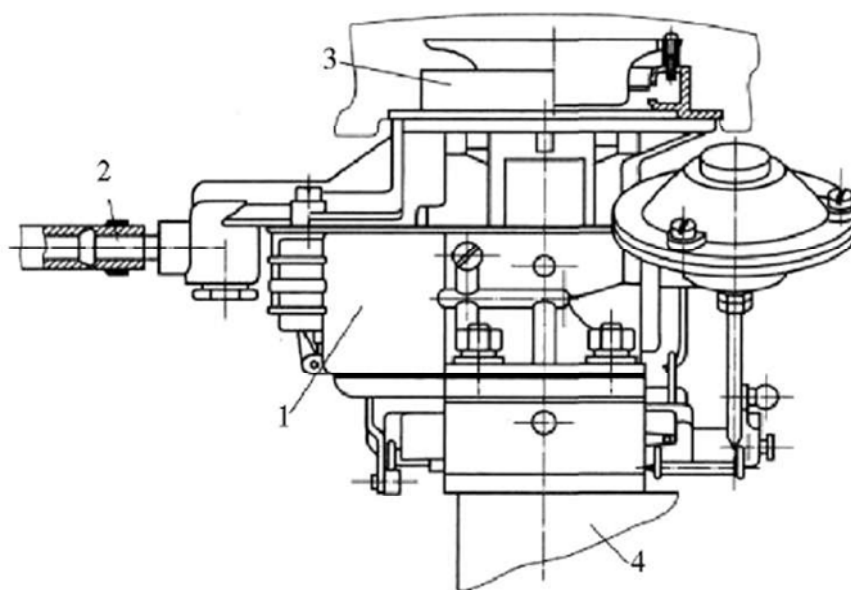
Газовый смеситель-насадка РЗАА на карбюраторе "Озон": 1 - корпус карбюратора; 2 - штуцер подвода бензина; 3 – насадка; 4 - впускной коллектор
